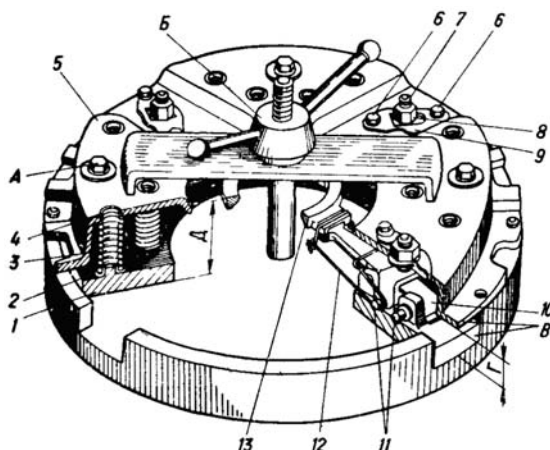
Разборка кожуха: 1 — диск нажимной; 2, 4 — стакан; 3, 12 — пружина; 5 — кожух; 6 — болт; 7 — вилка; 8 — гайка; 9 — пластина; 10 — рычаг; 11 — ось; 13 — кольцо упорное; А — болт технологический; Б — приспособление; В — метка; Г, Д — размер
